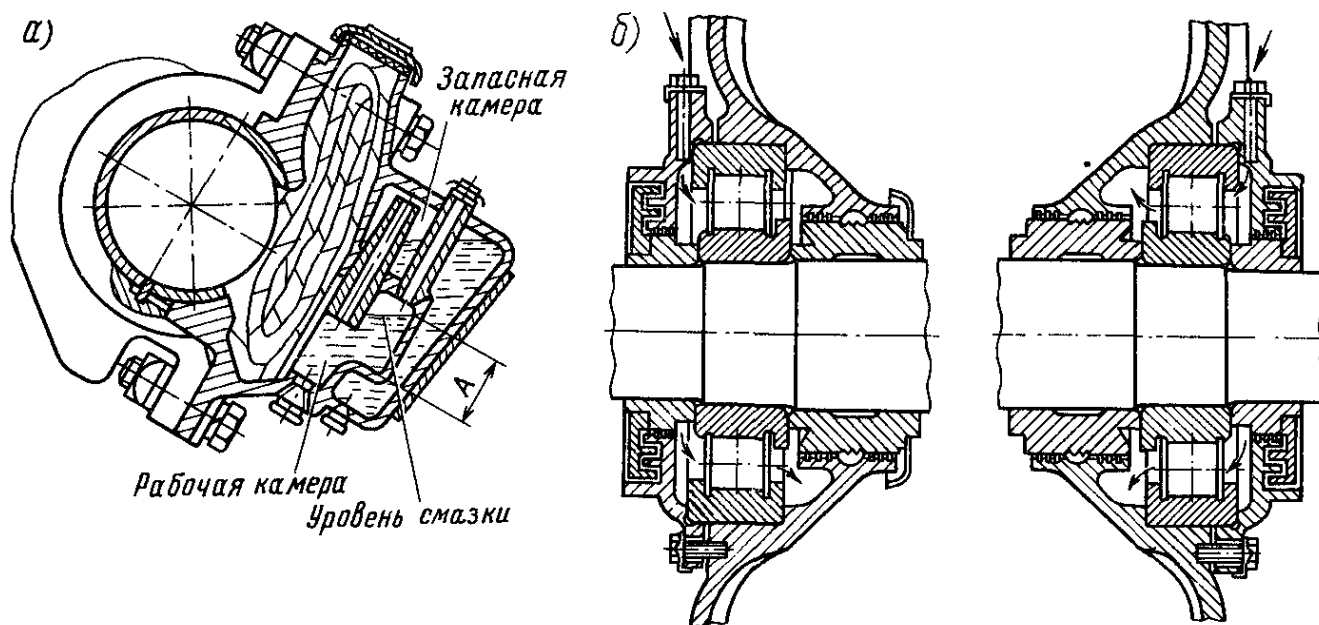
Схема смазки подшипников тягового двигателя НБ-406Б:
